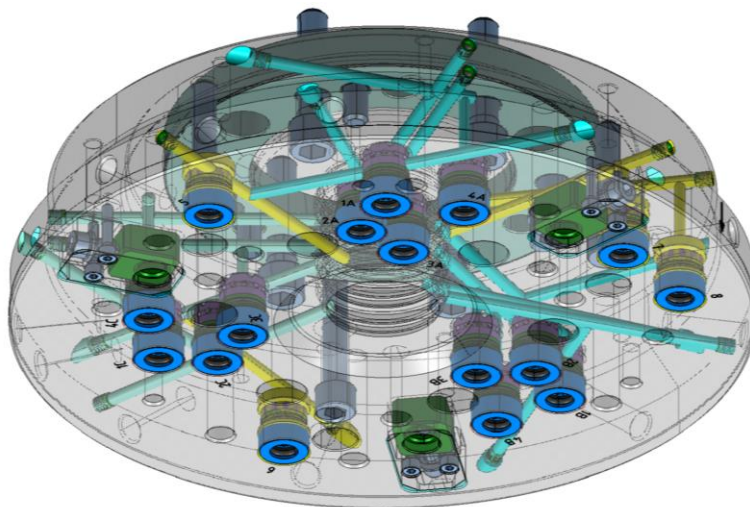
Univerzální adaptér osazený kroužky č. 24162000 a 24182010 od firmy SMW Autoblok
